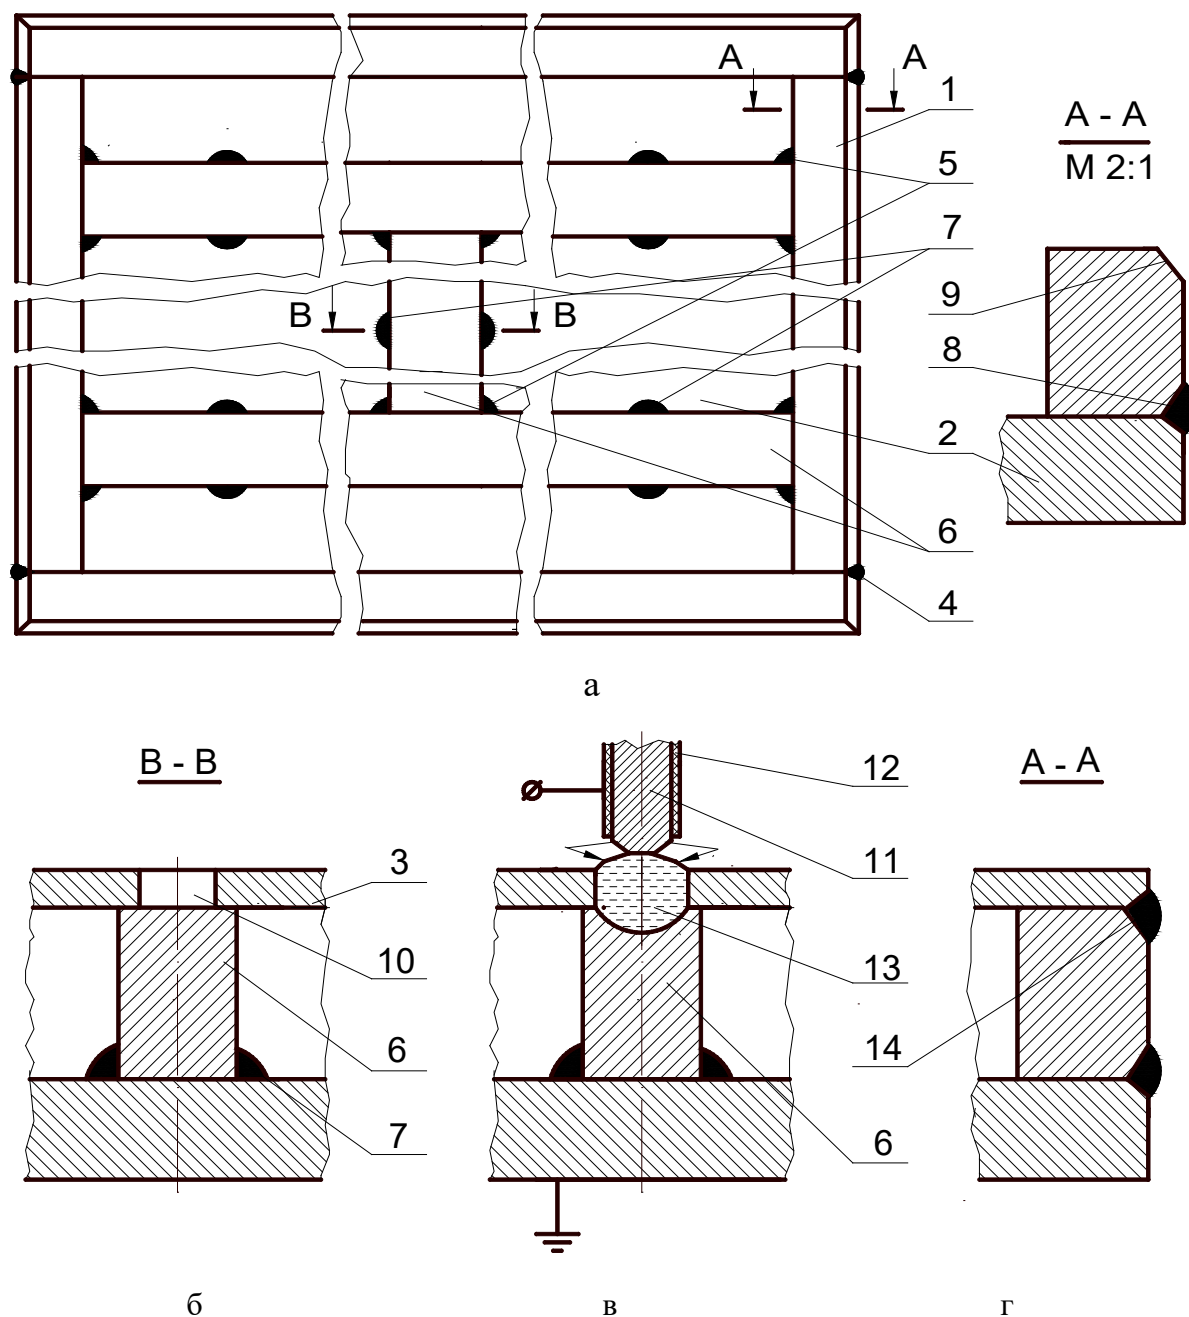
Процес виготовлення полегшеного біметалу зі звареною пластиною основи
